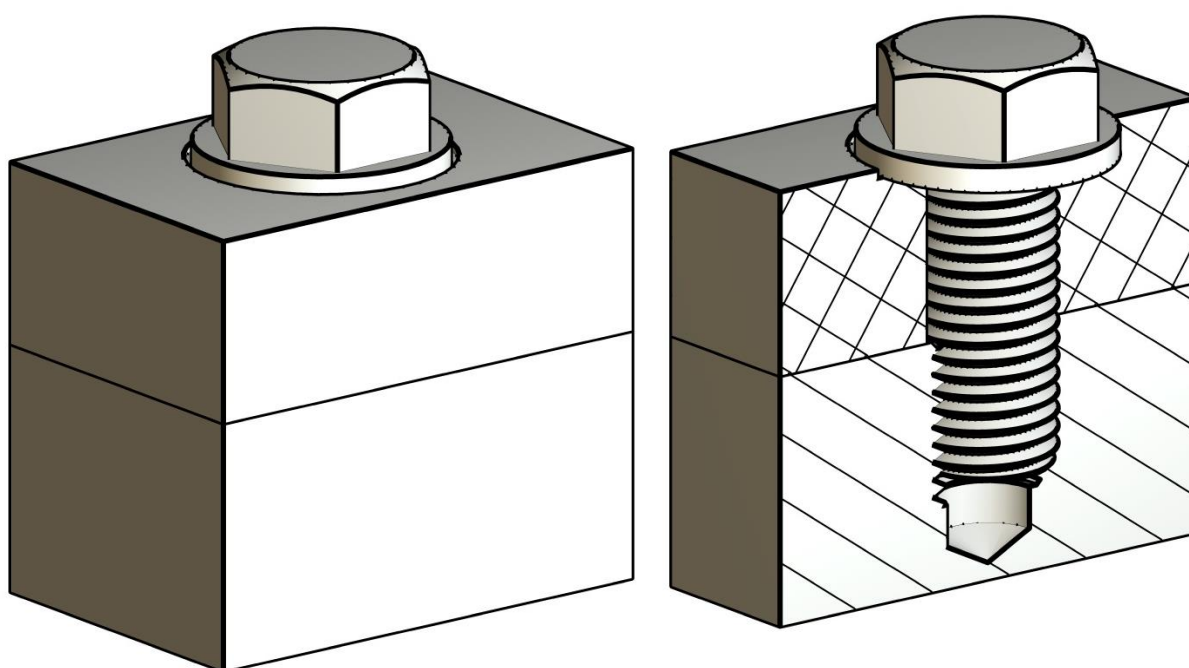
Соединение деталей стандартными крепежными изделиями – винтом с шестигранной головкой (ГОСТ 7798-70) и круглой шайбой (ГОСТ 11371-78), предотвращающей повреждение верхней прикрепляемой неметаллической детали головкой винта (справа изображение выполнено условно в разрезе)
